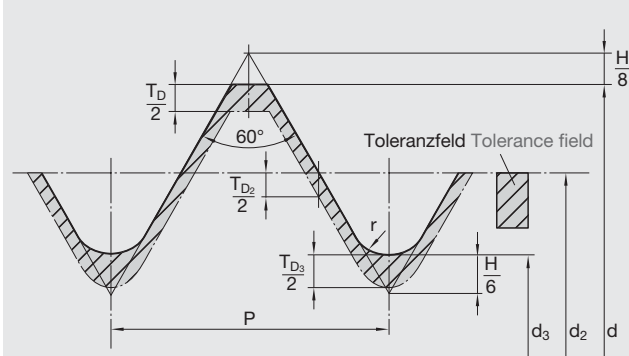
Bolzensgewinde mit Grundabmaß 0
